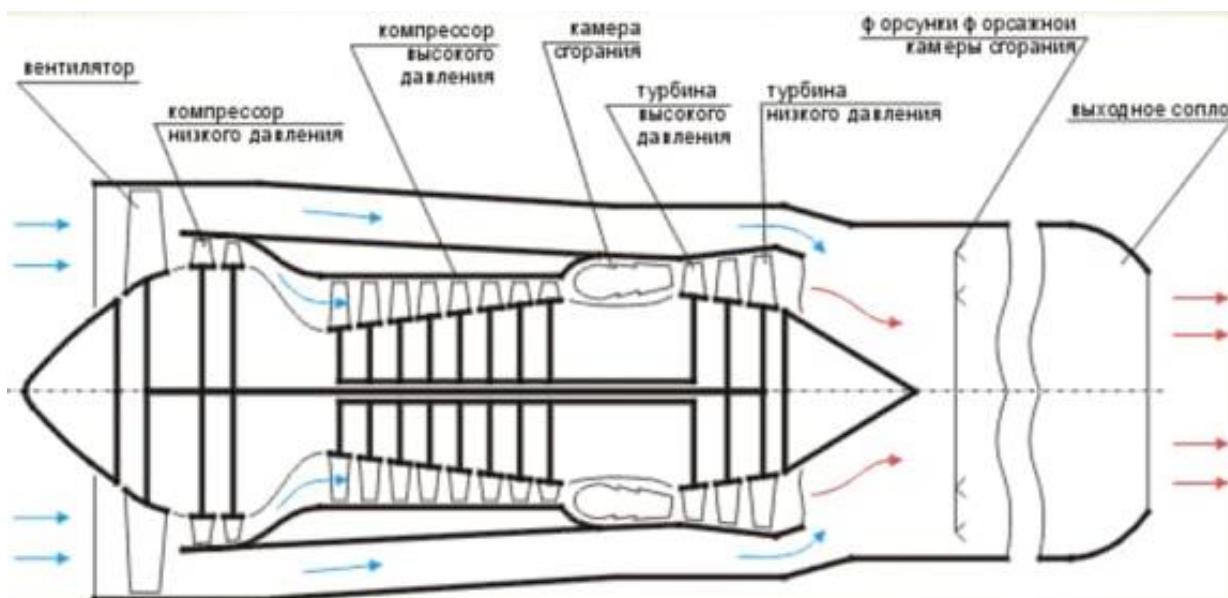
Схема двухконтурного турбореактивного двигателя.
